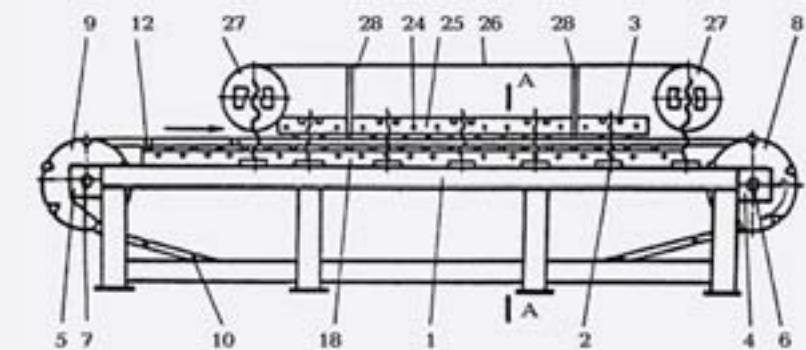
Пресс для непрерывного изготовления профильных изделий
